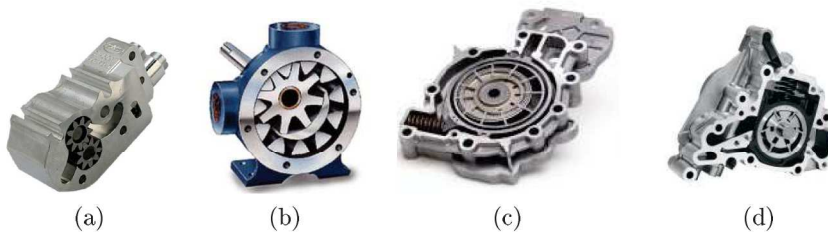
a) Bomba de óleo engrenagens dentado externo S&S [8]; b) Bomba de óleo engrenagens dentado interno [9]; c) Bomba de óleo de palhetas Stackpole [10]; d) Bomba de óleo de alhetas MAHLE [11].
